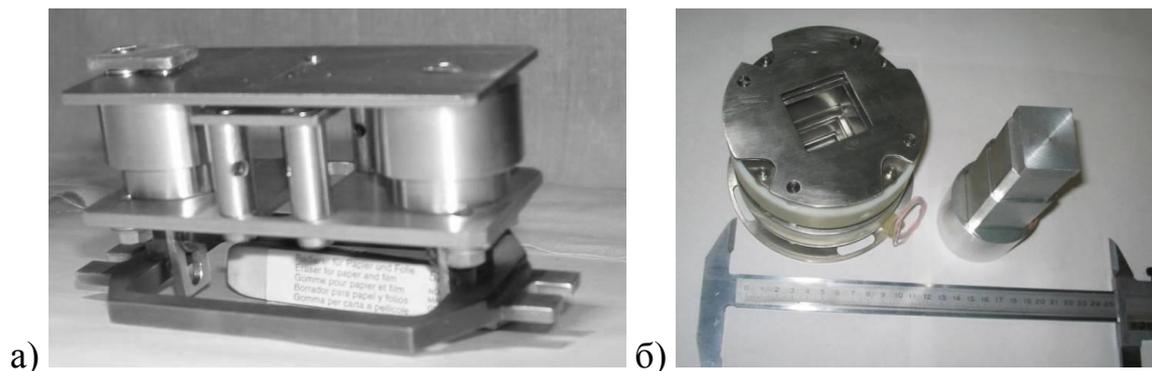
Фотографии: а) системы формирования пучка в сборе; б) электростатической линзы в сборе вместе с приспособлением для сборки
